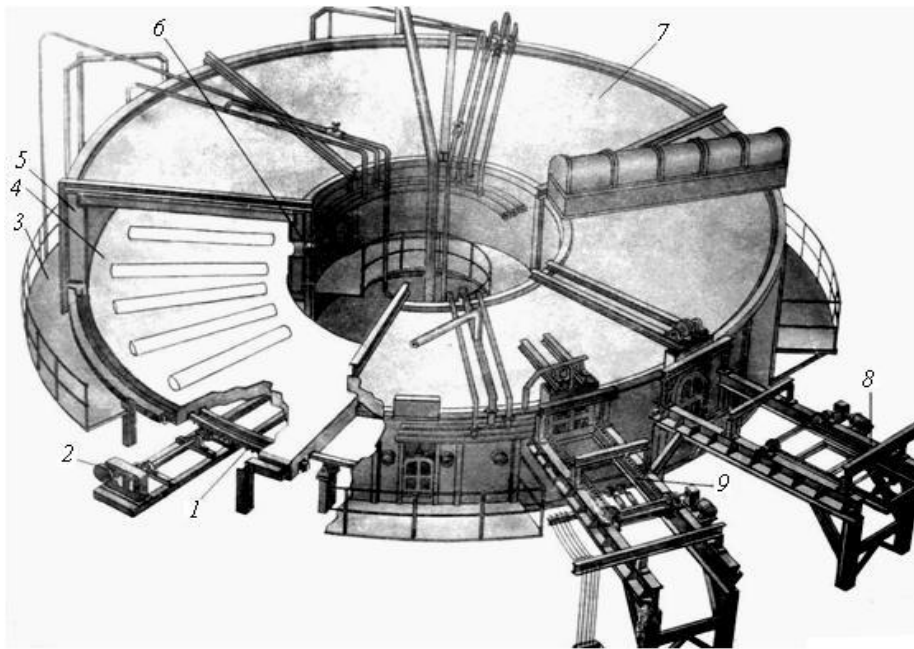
Схема карусельної печі: 1-зубчаста рейка; 2-пристрій привода руху черена печі; 3-робочий майданчик; 4-обертальний черен; 5-корпус печі; 6-високотемпературна зона; 7-зона розігріву; 8-завантажувальний пристрій; 9-вивантажувальний пристрій заготовок
